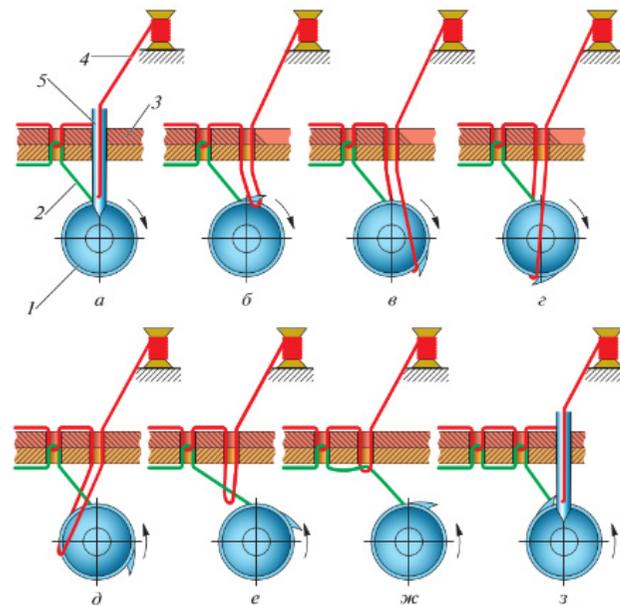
Процесс образования двухниточного челночного стежка: 1 — челнок; 2 — нитка челнока; 3 — шиваемый материал; 4 — нитка иглы; 5 — игла
